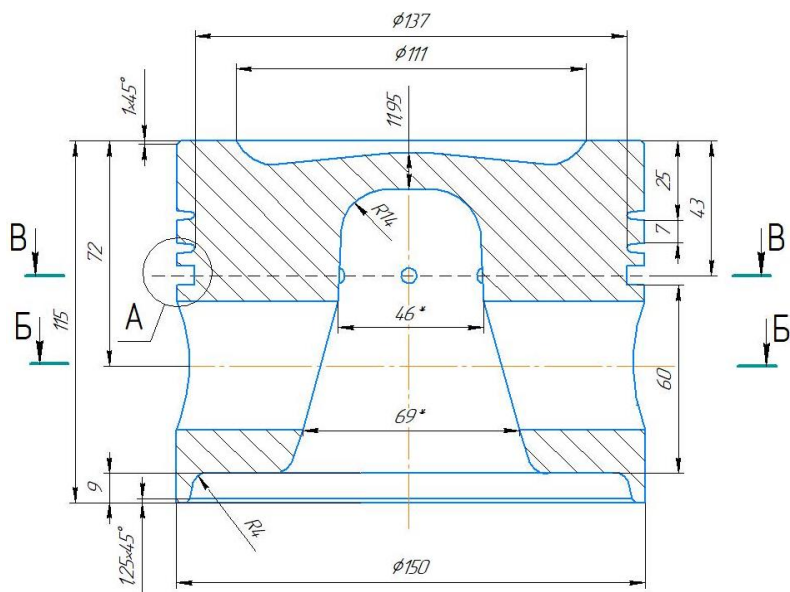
Эскиз поршня с изменённой конструкцией
